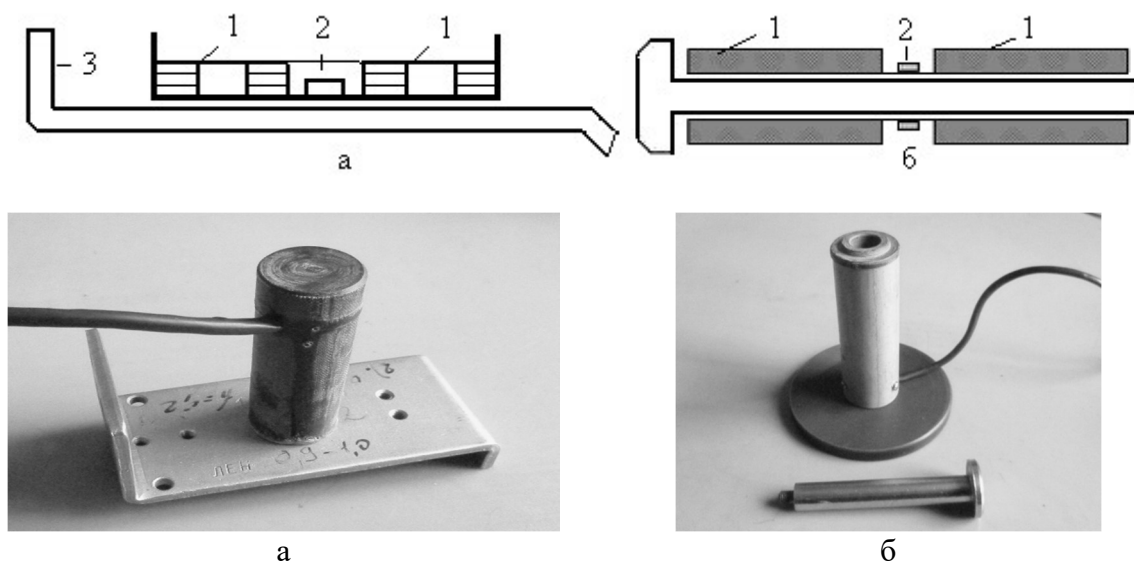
Датчики для контроля изделий плоской и цилиндрической форм.
